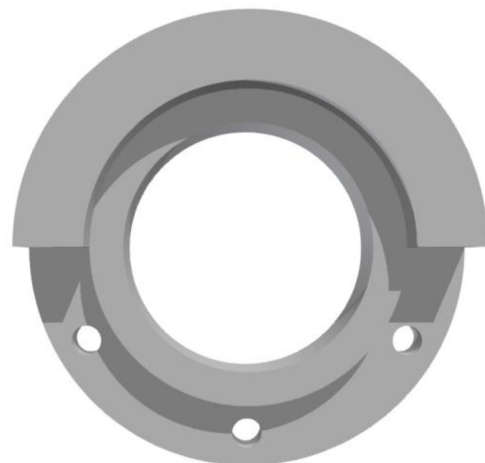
Zkompletované kryty spojené šroubovými spoji.
